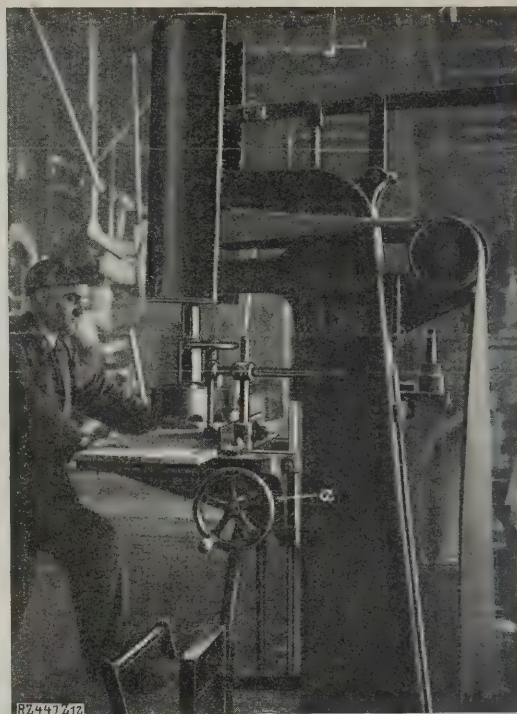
Schwere Bohrmaschine mit Trommelsäge.
